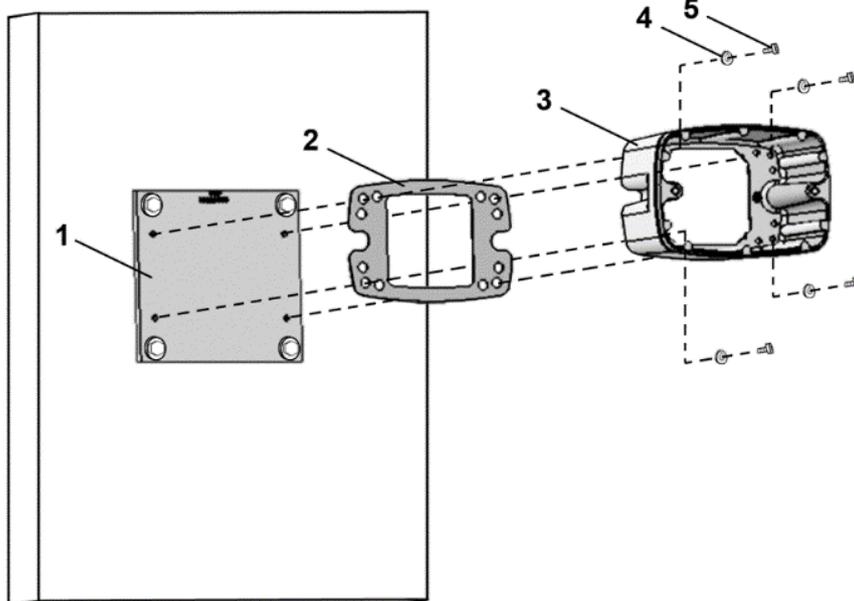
Befestigung des Becher BG. D an der Adapterplatte
